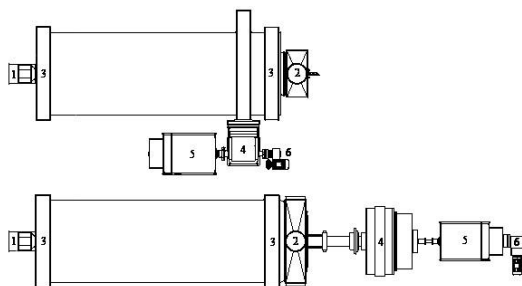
Компоновка современных шаровых мельниц: 1 – загрузка мельницы, 2 – разгрузка мельницы, 3 – опоры башмаков подшипников скольжения, 4 – главный редуктор, 5 – двигатель мельницы, 6 – вспомогательный привод
